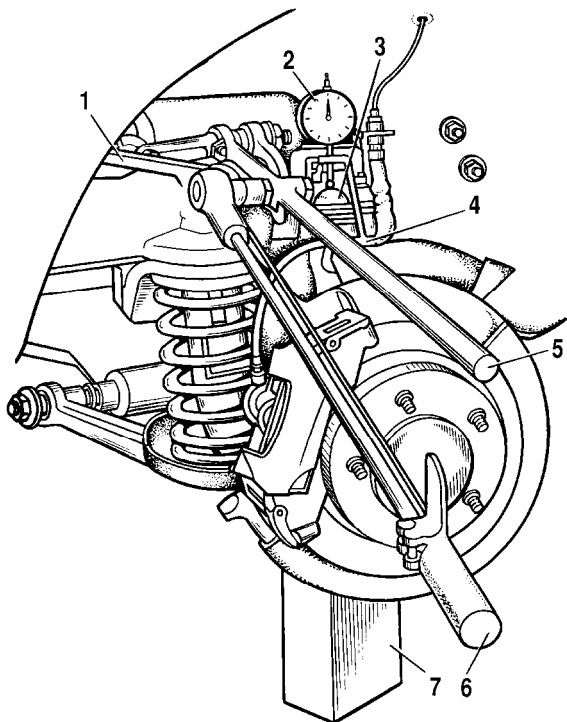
Проверка состояния резинометаллического шарнира рычага передней подвески:
